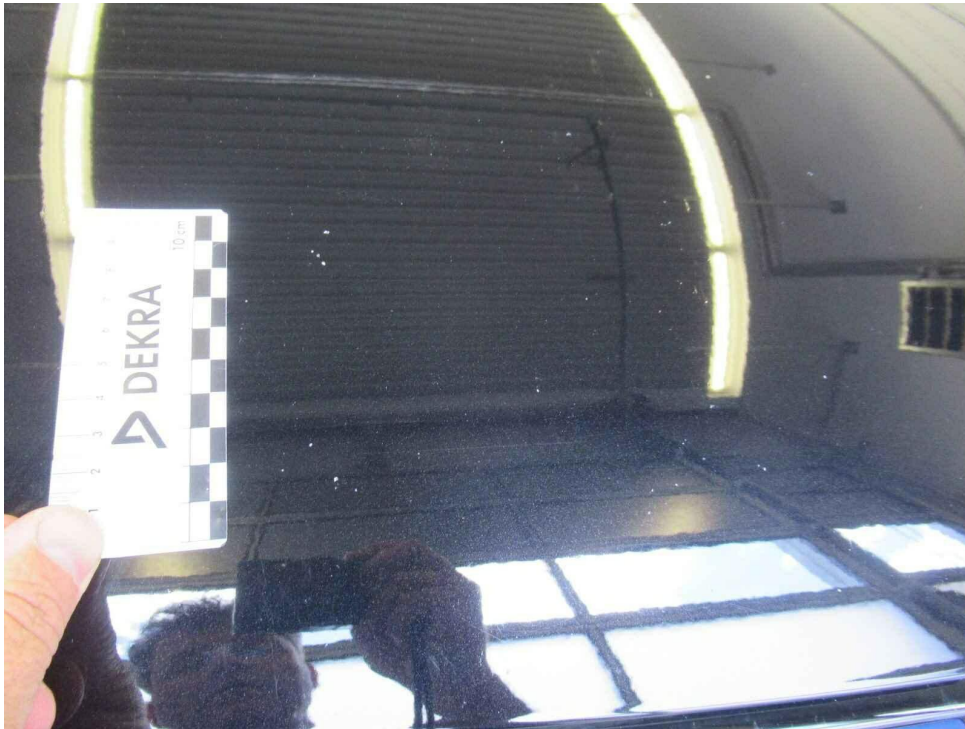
Motorhaube Lackierung, viele Steinschläge, Gebrauchsspur
